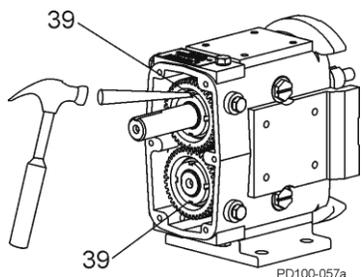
Plier la languette de verrouillage sur les rondelles de blocage
